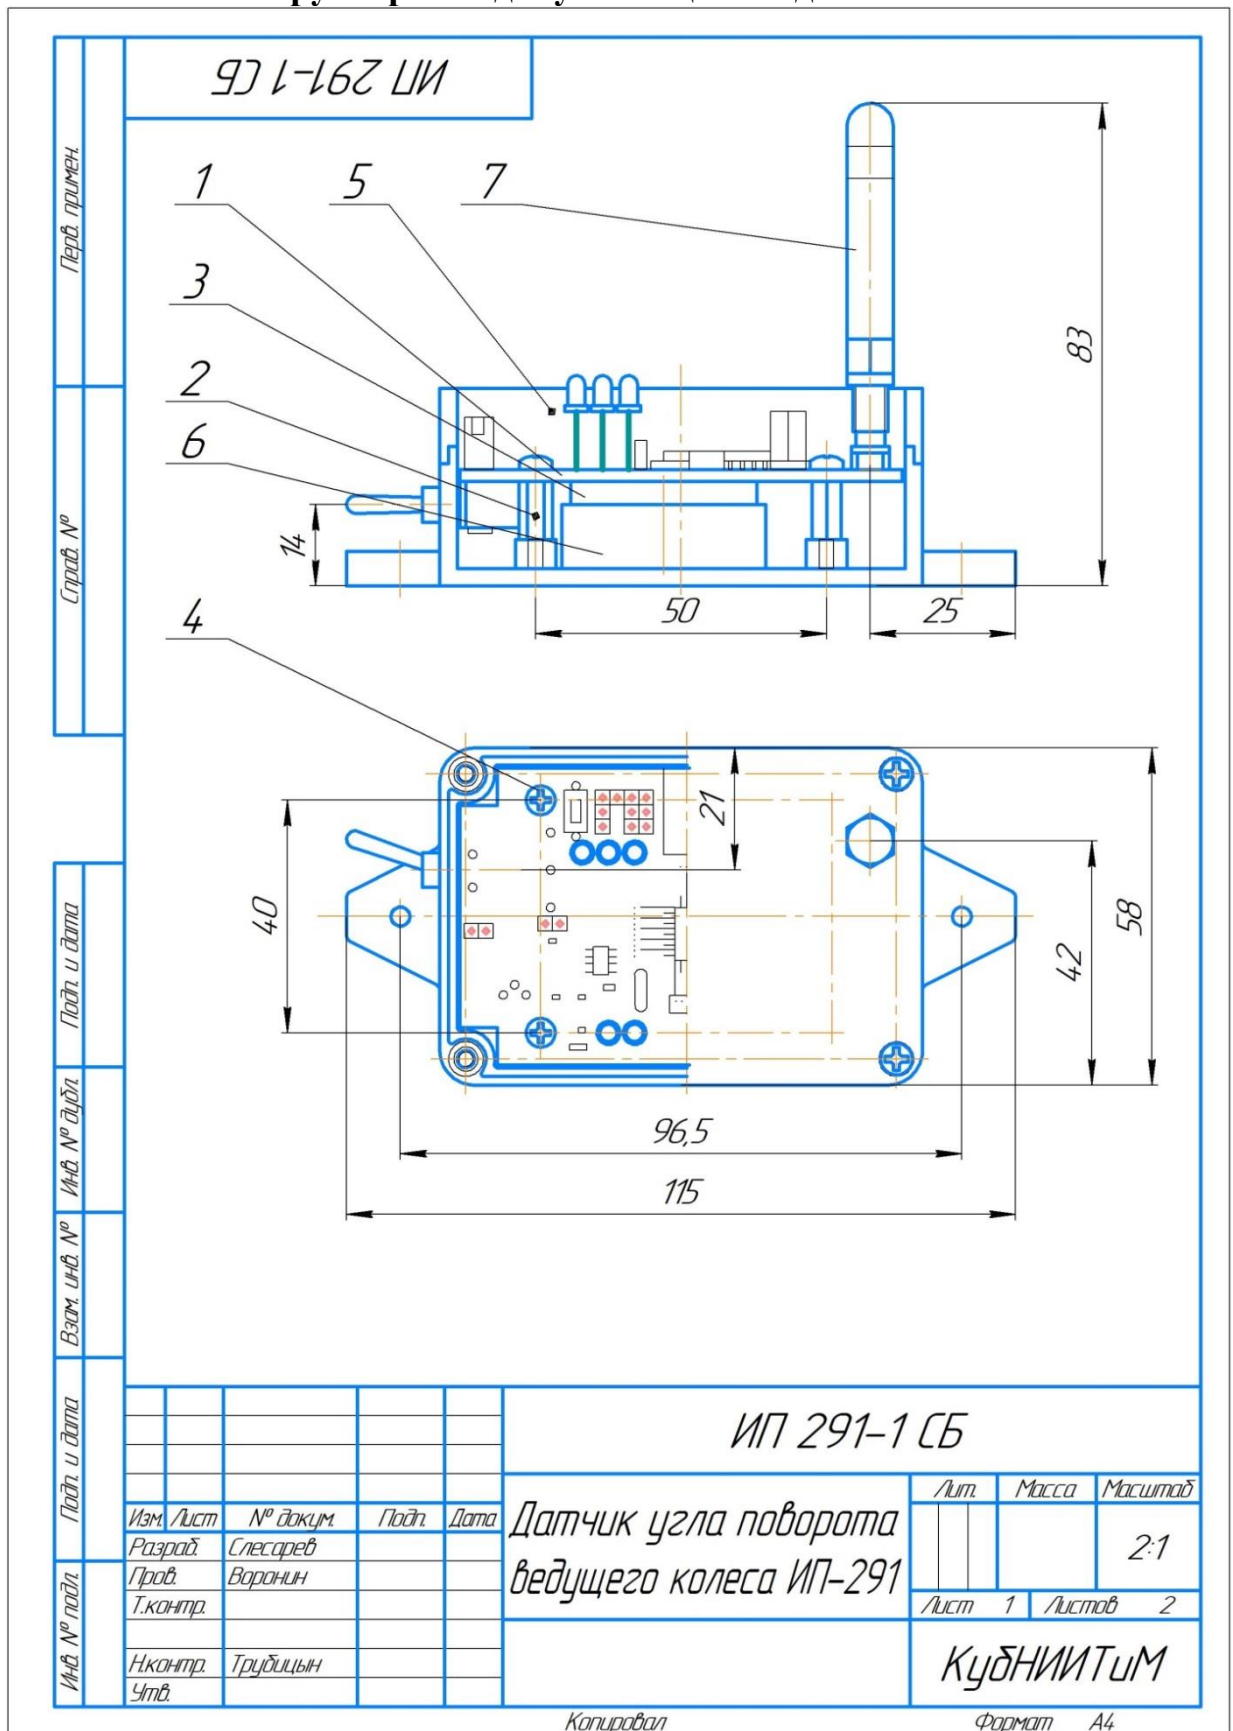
Сборочный чертёж датчика ИП-291
